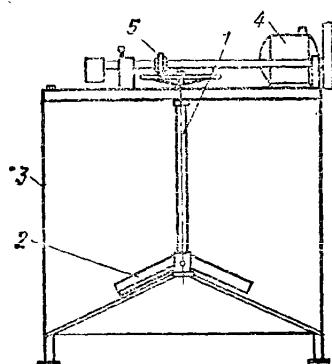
Приспособление для приготовления сиропа к медогонке МР-50А
